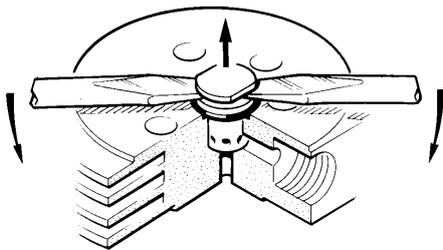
Válvula de presión 3ª etapa, desmontaje
